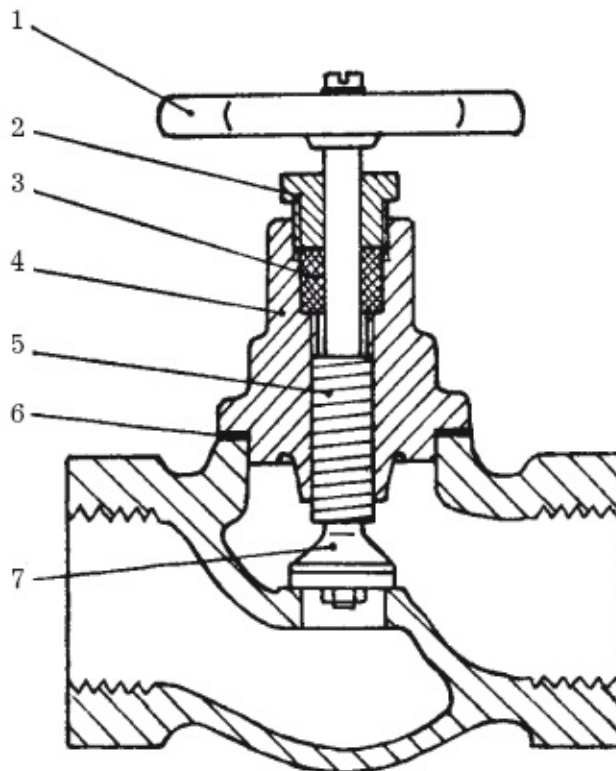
Устройство вентиля: 1 – маховик; 2 – втулка; 3 – набивка сальника; 4 – корпус головки; 5 – резьба штока; 6 – изоляция; 7 – клапан с прокладкой
